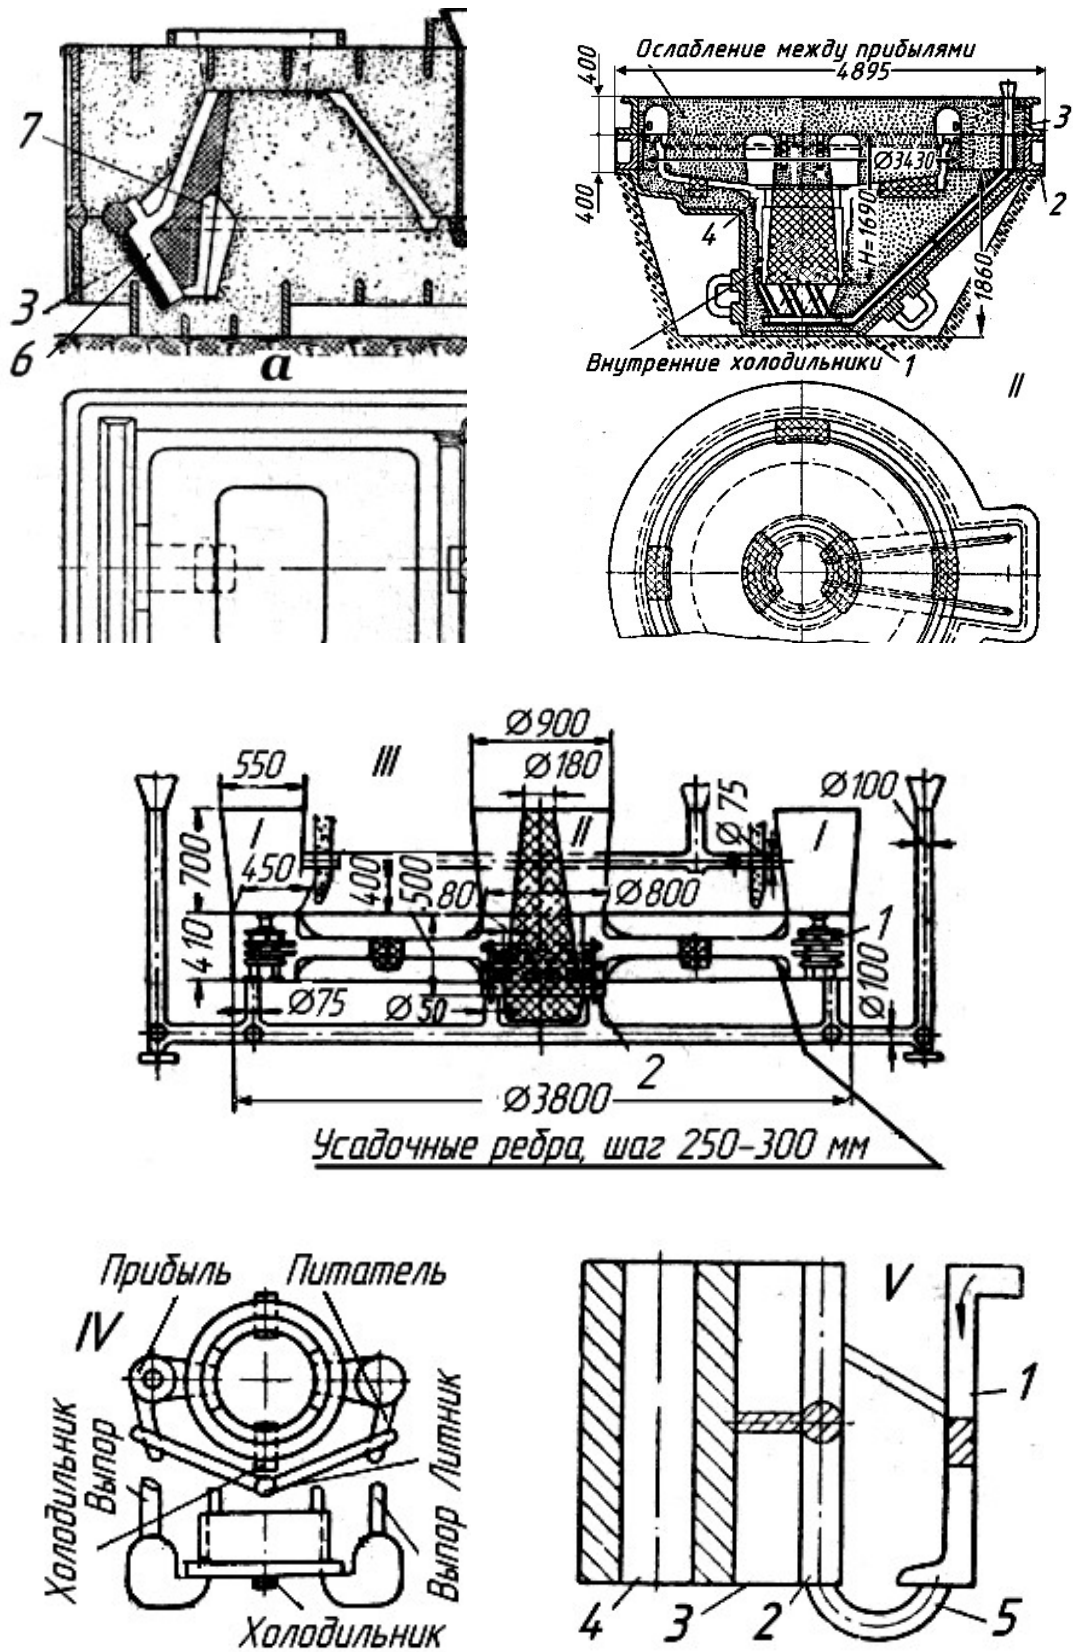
Схемы литниковых устройств для стальных отливок
